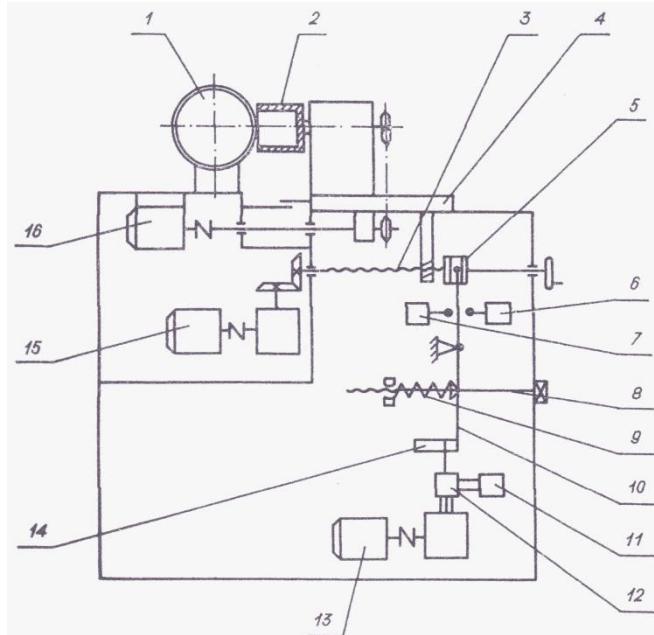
Кинематическая схема экспериментального стенда: 1 – круг; 2 – заготовка; 3 – ходовой винт; 4 – стол; 5 – обойма; 6, 7 – концевые выключатели; 8, 9 – механизм регулирования усилия подачи; 10 – рычаг; 11 – электромагнит; 12 – муфта; 13 – привод прерывистой подачи; 14 – кулачок; 15 – привод подачи стола; 16 – привод вращения заготовки
